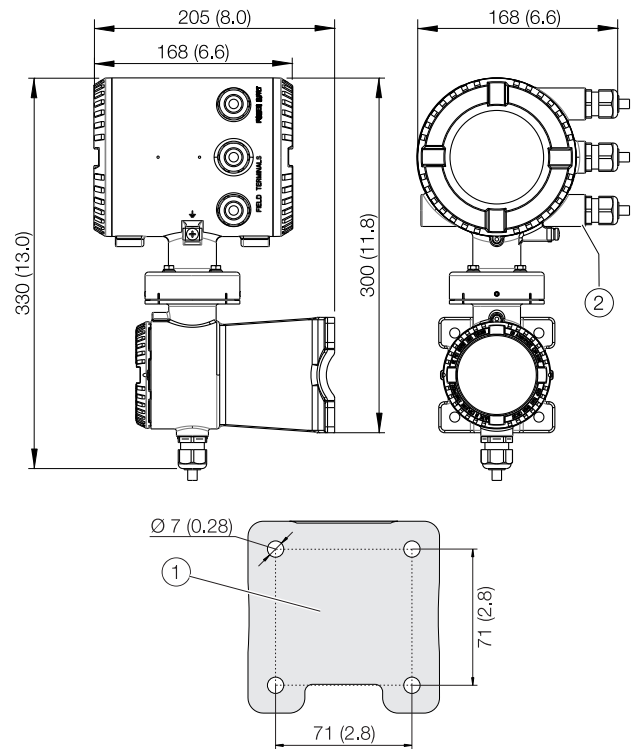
Montageabmessungen Zweikammer-Gehäuse
